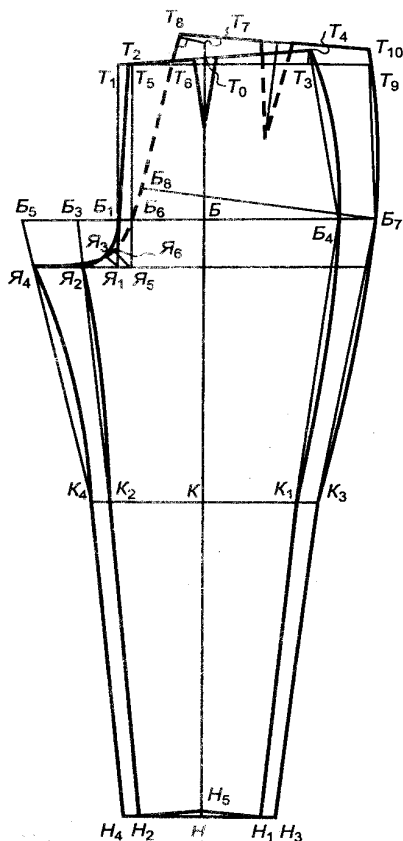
Креслення базової конструкції жіночих штанів
